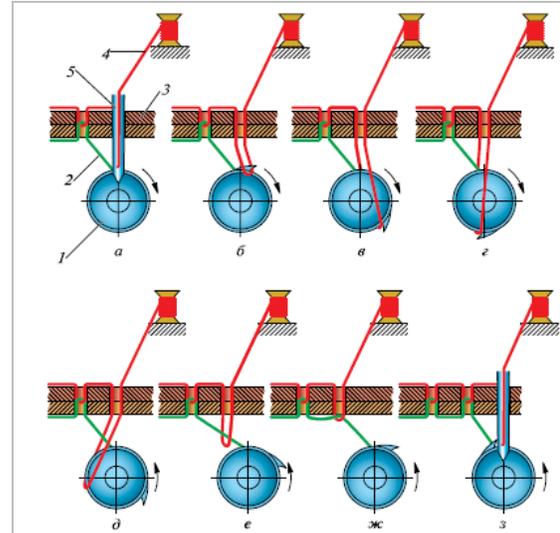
Процесс образования двухниточного челночного стежка: 1 — челнок; 2 — нитка челнока; 3 — сшиваемый материал; 4 — нитка иглы; 5 — игла
